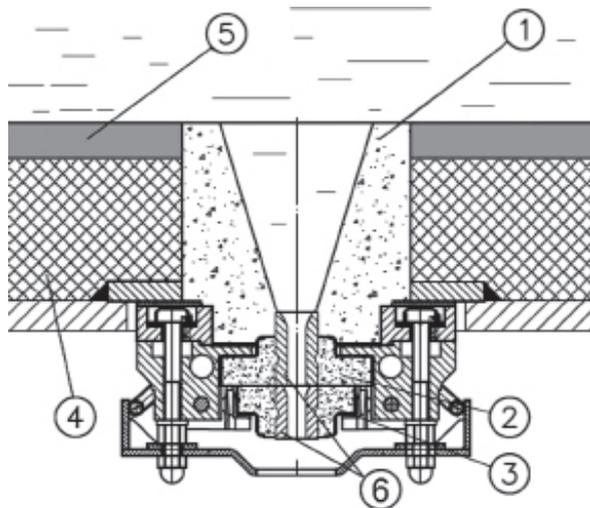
Разливочный узел промковша сортовой МНЛЗ с системой CNC быстрой замены стаканов-дозаторов: 1 – воронка из набивной массы или формованный гнездовой блок; 2 – верхний стакан-дозатор типовой конструкции; 3 – нижний (сменный) стакан-дозатор; 4 – постоянная футеровка; 5 – рабочий (возобновляемый) слой футеровки; 6 – ZrO_2 – вставки в стаканах-дозаторах
